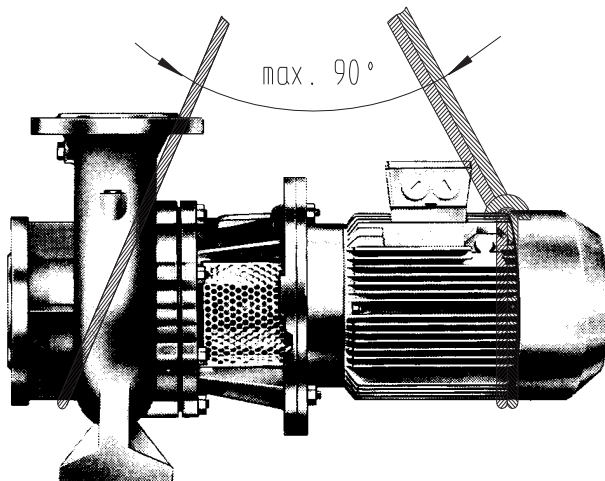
Hebezeug befestigen an Pumpenaggregat
